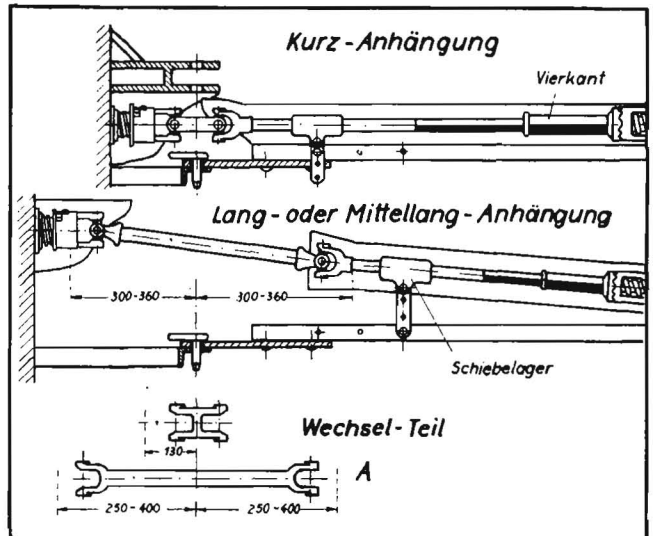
Umstellung einer Zapfwellen-Kurzanhängung in Langanhängung
